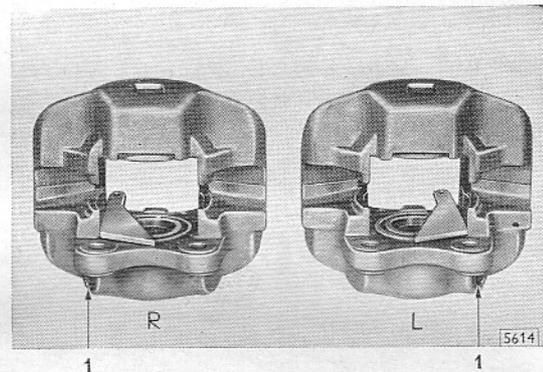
Einbaulage der Kolben im Flansch- und Deckelgehäuse des linken und rechten Bremssattels
